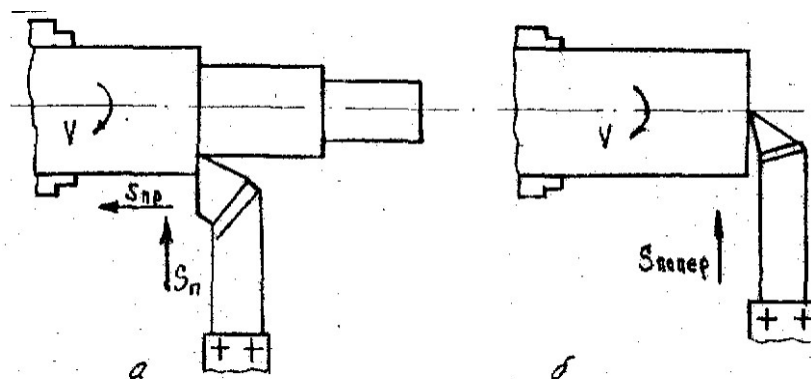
Схеми різання на токарних верстатах: а) обточування ступінчастих валів; б) підрізання торця
